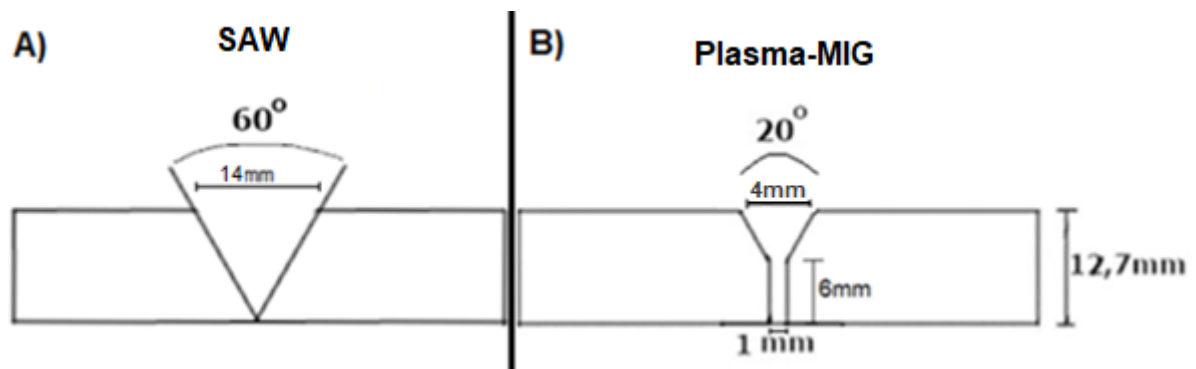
Junta utilizada para posterior soldagem de tubo com o processo Plasma-GMAW, em comparação a juntas comumente soldada pelo processo SAW.
